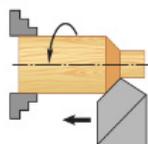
Закрепление заготовки в трёхкулачковом патроне
